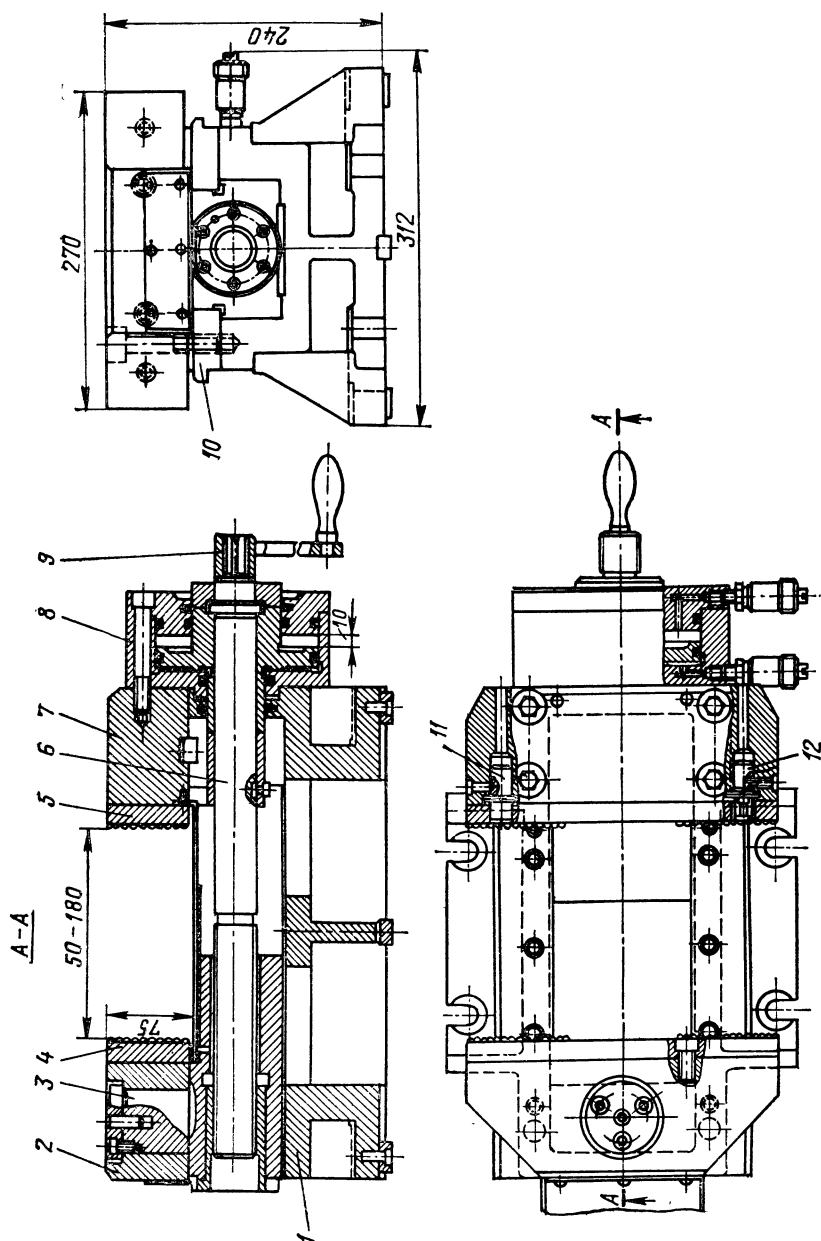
Специализированное переналаживаемое приспособление тисочного типа к фрезерным станкам
